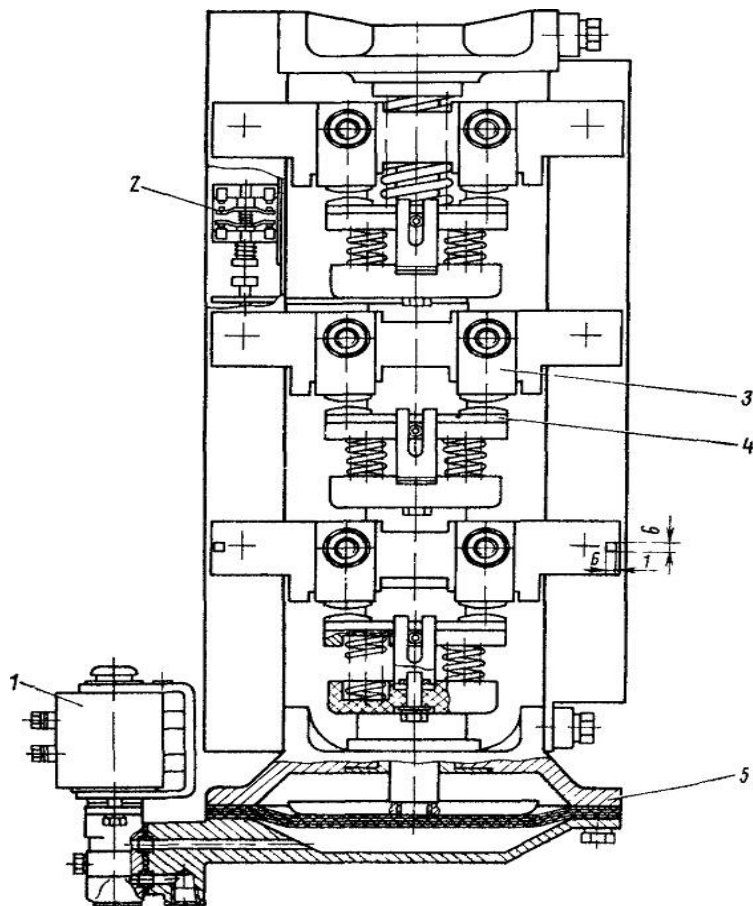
Контактёр электропневматический групповой ПКГ-566М: 1 — вентиль электропневматический; 2 — блокировочный контакт; 3 — неподвижный контакт (силовой); 4 — подвижной контакт (силовой); 5 — пневматический привод
